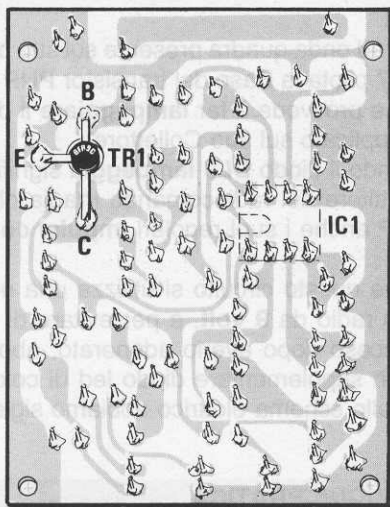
Sul lato rame dello stampato dovete applicare il transistor BFR.90 rivolgendo il terminale più lungo del Collettore sulla pista in basso.
